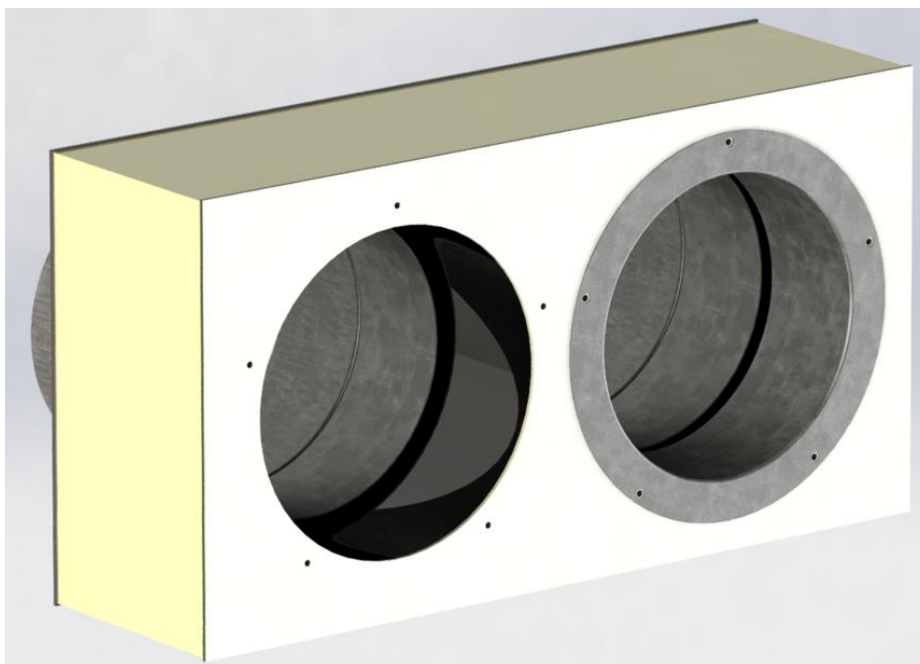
Разметка отверстий крепления фланцев внутренней стенки.
